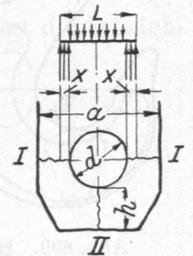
Hängelasche der Hakenflasche Abb. 899.
